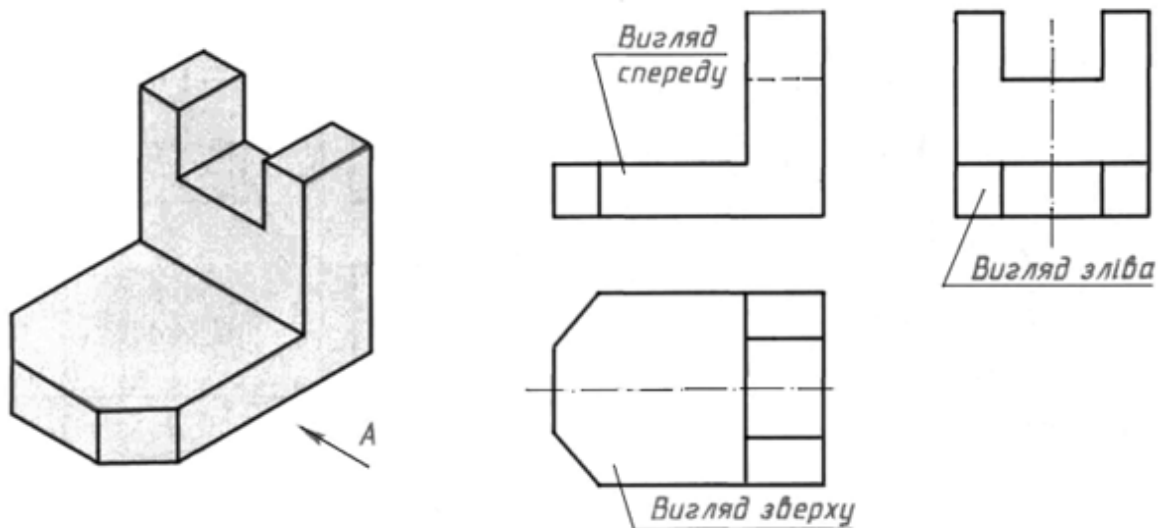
Креслення деталі, яке складається з трьох видів
